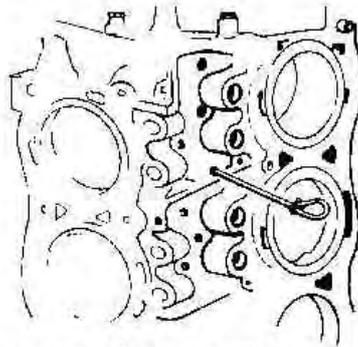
В.5. Извлечение толкателей при помощи куска проволоки (Разд.9)
